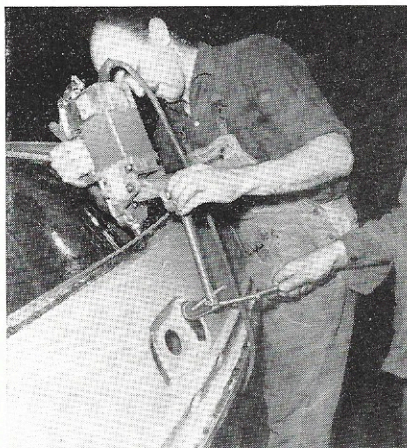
Soudage panneau arrière sur renfort de coffre. Pince ARO. Pour éviter de marquer la tôle, interposer une palette entre celle-ci et l'électrode.
